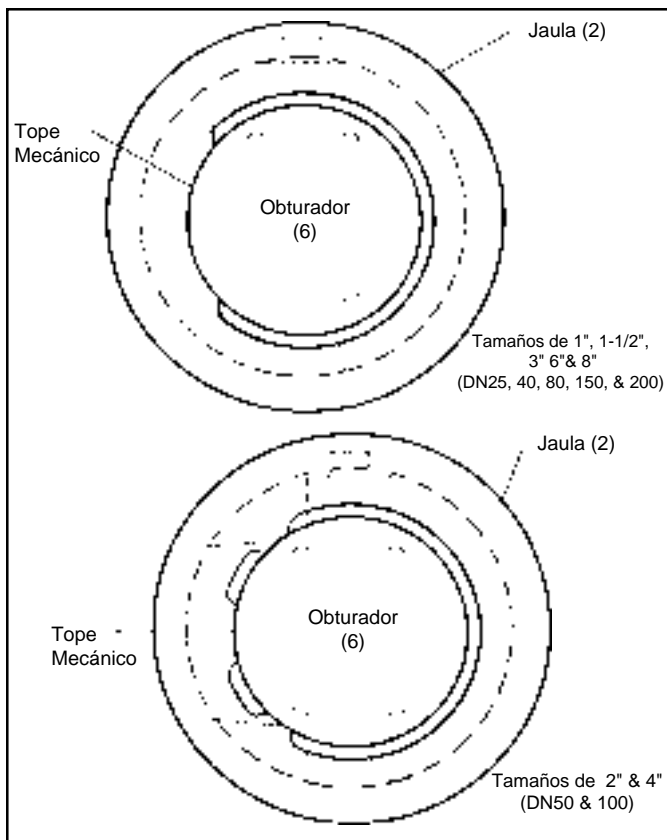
Mecanismos de Tope de Recorrido — Obturador en Posición de Cierre vista Frontal - Posterior
